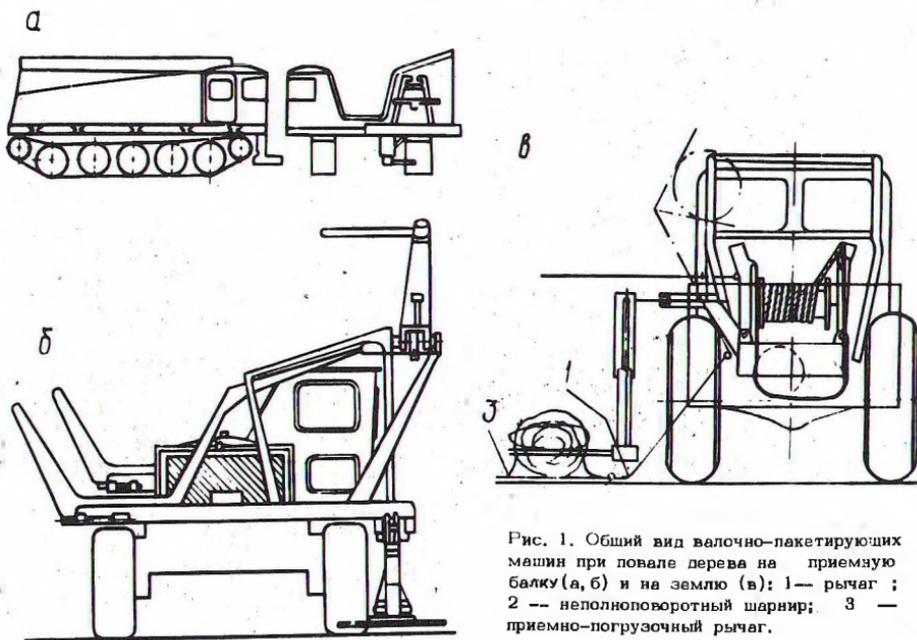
Общий вид валочно-пакетирующих машин при повале дерева на приемную балку (а, б) и на землю (в): 1 — рычаг; 2 — полноповоротный шарнир; 3 — приемно-погрузочный рычаг.
